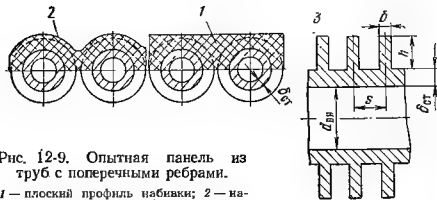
Опытная панель из труб с поперечными ребрами.
